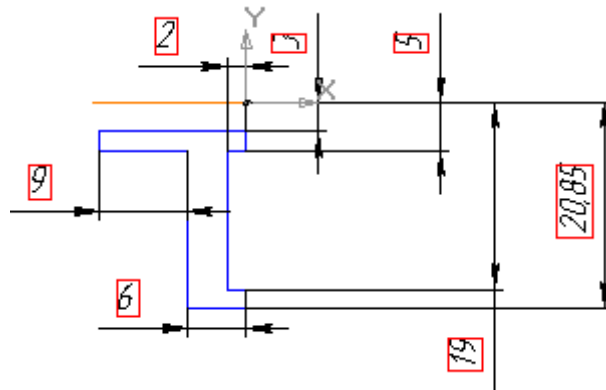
Ескіз заготовки зубчастого колеса
